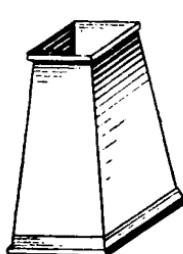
Переход с прямоугольного на прямоугольное сечение
